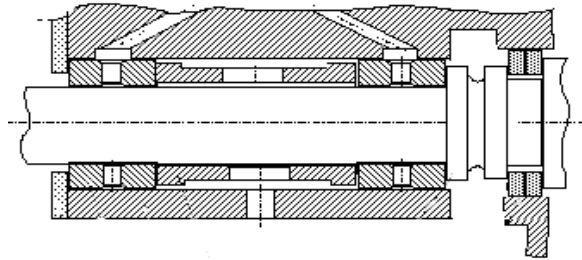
Конструкция серийного подшипника турбокомпрессора ТКР-8,5 с ПВ штулками
